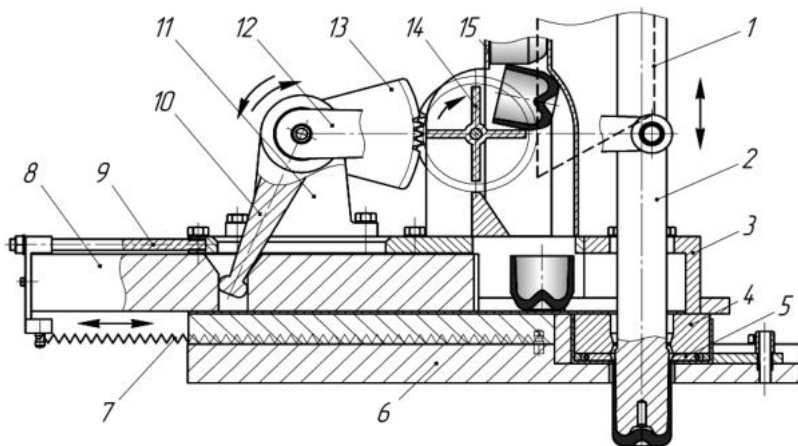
Конструкция шиберного питателя: 1 – нажимная пластина; 2 – пуансон; 3 – крышка; 4 – матрица; 5 – съёмник; 6 – основание; 7 – пружина; 8 – шибер; 9 – направляющая; 10, 12 – рычаги; 11 – кронштейн; 13 – зубчатая передача; 14 – отсекатель; 15 – лоток-магазин
